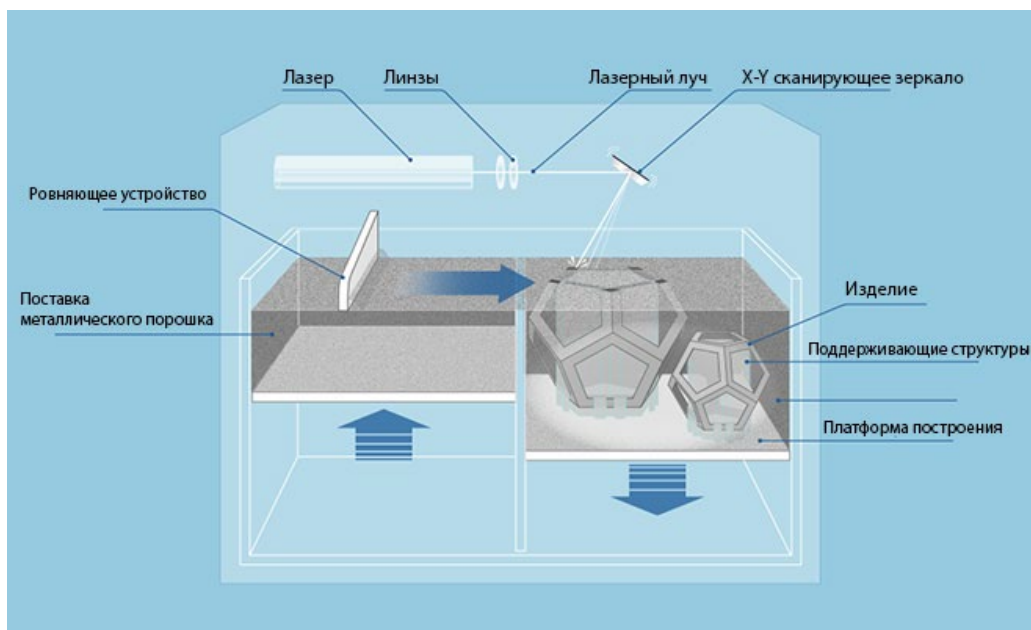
Схема процесу вибіркового лазерного плавлення (Selective Laser Melting – SLM)
